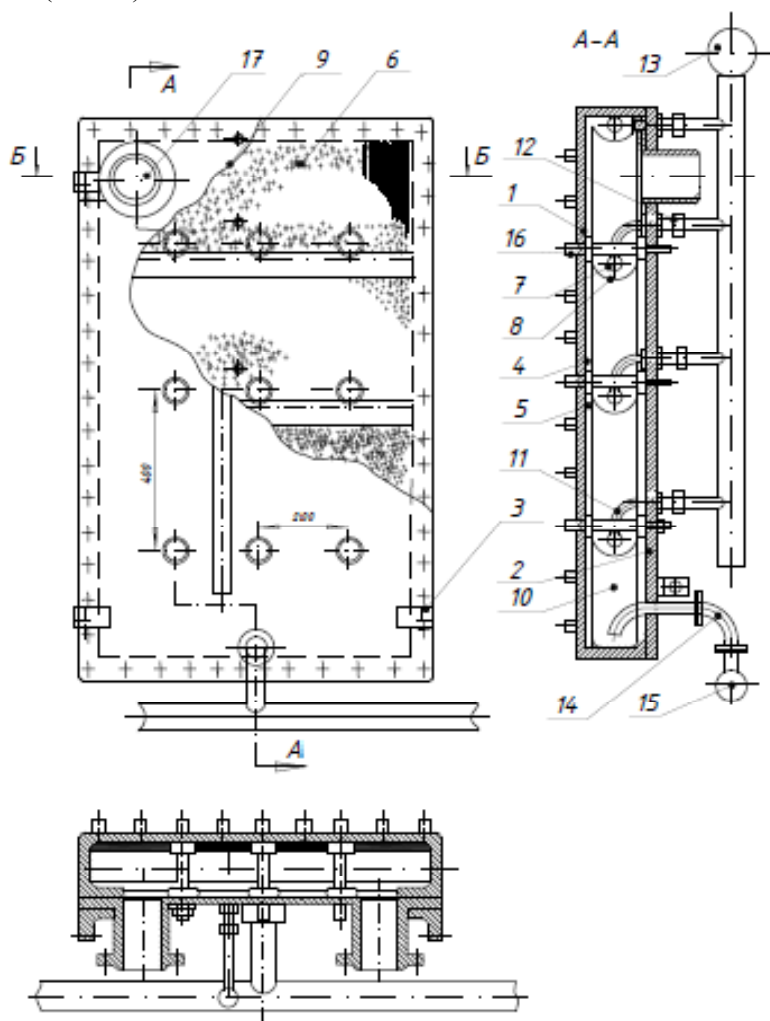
Схема охлаждения кессона капиллярно-пористой системы с распорками: 1 - корпус; 2 - крышка; 3 - болт; 4 - стенка; 5 - капиллярно-пористая структура; 6 - пластина; 7 - артерия; 8 - корытце; 9 - отверстие; 10 - канал; 11, 17 - патрубок; 12 - труба; 13, 15 - коллектор; 14 - сифон; 16 - распорки
